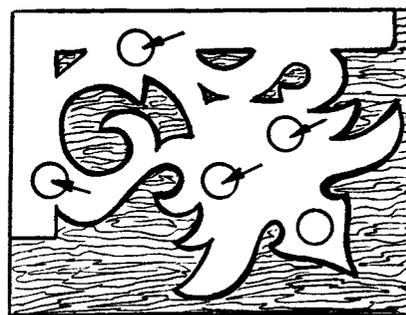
Подготовка отверстий для вставки полотна пилы.
